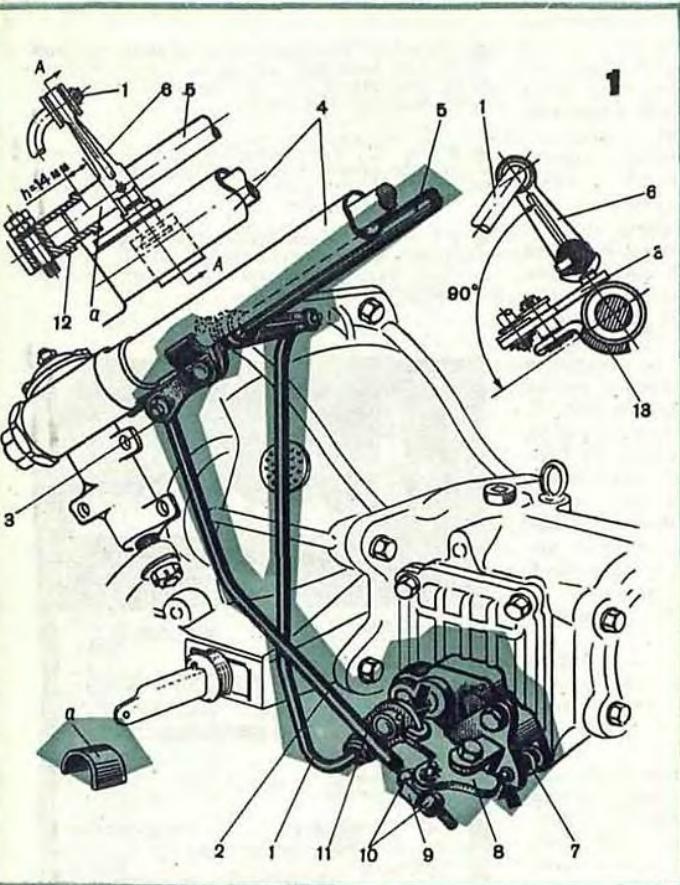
Привод управления коробкой передач модели 407: 1 и 2 — поводковые тяги; 3 и 8 — рычаги управления поводковыми тягами; 4 — труба рулевой колонки; 5 — вал управления коробкой передач; 7 — упор против случайного включения заднего хода; 8 и 11 — рычаги управления валиком переключателя; 9 — регулировочный сухарь; 10 — контргайки; 12 — кронштейн вала управления; 13 — кронштейн с осью для рычага 3; а — вкладыш для фиксирования длины тяги 2.
